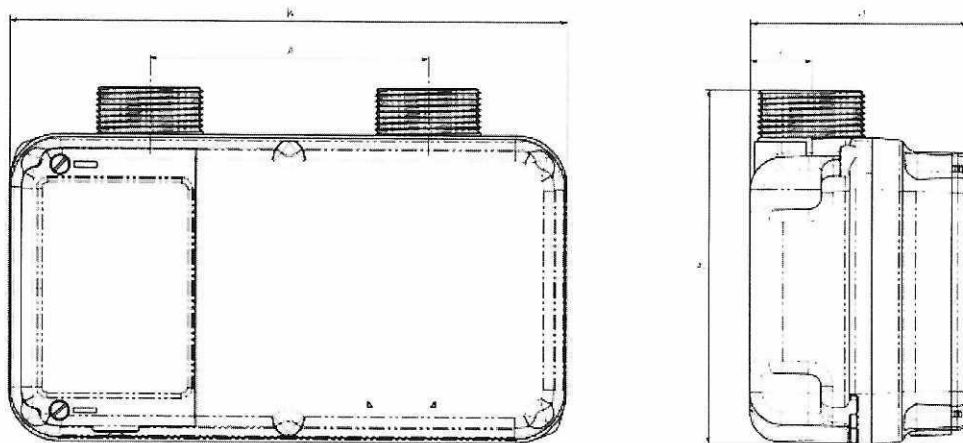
Габаритные и присоединительные размеры Модели 1
